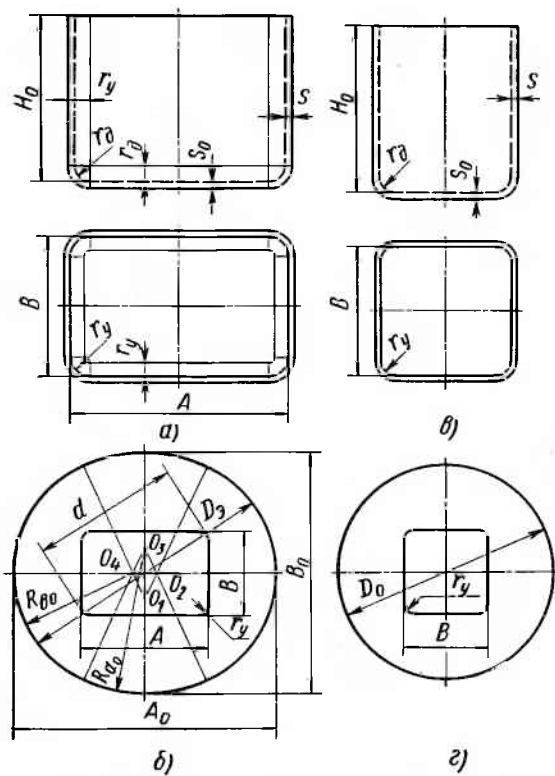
Чертежи коробчатых деталей и контуры заготовок для них:
